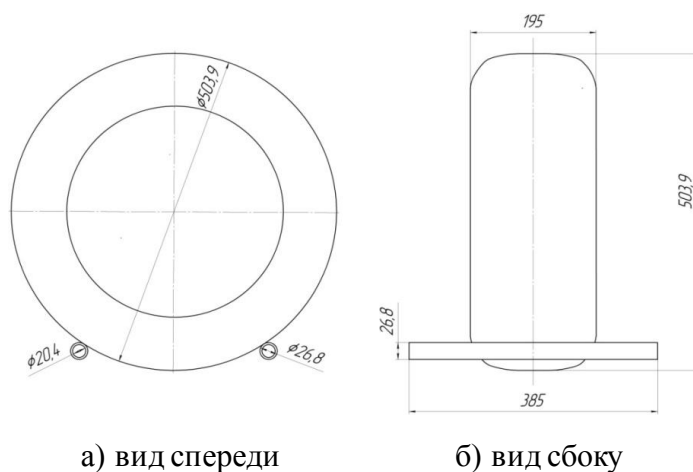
Вид колеса и продольных труб для фиксации колеса
